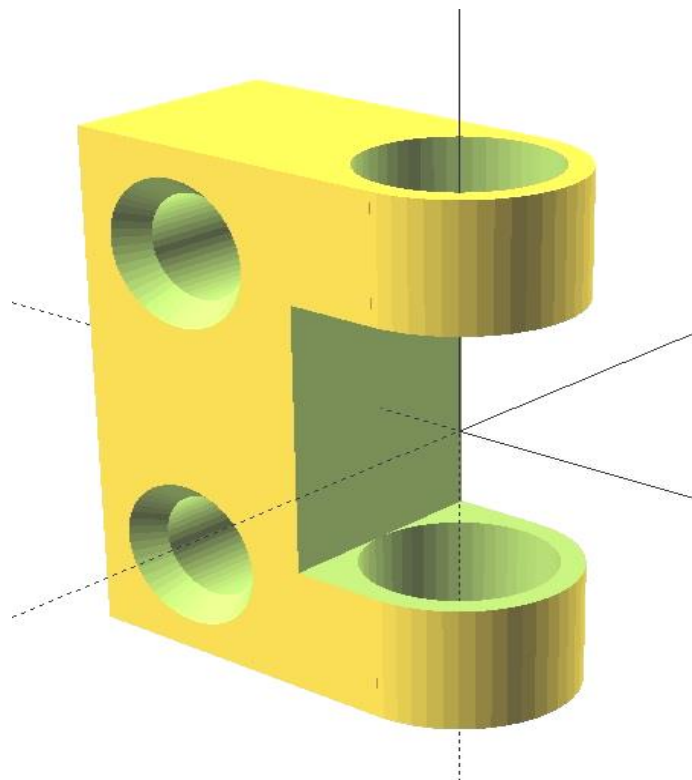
Чертеж приспособление для установки пилочки на лобзик.
